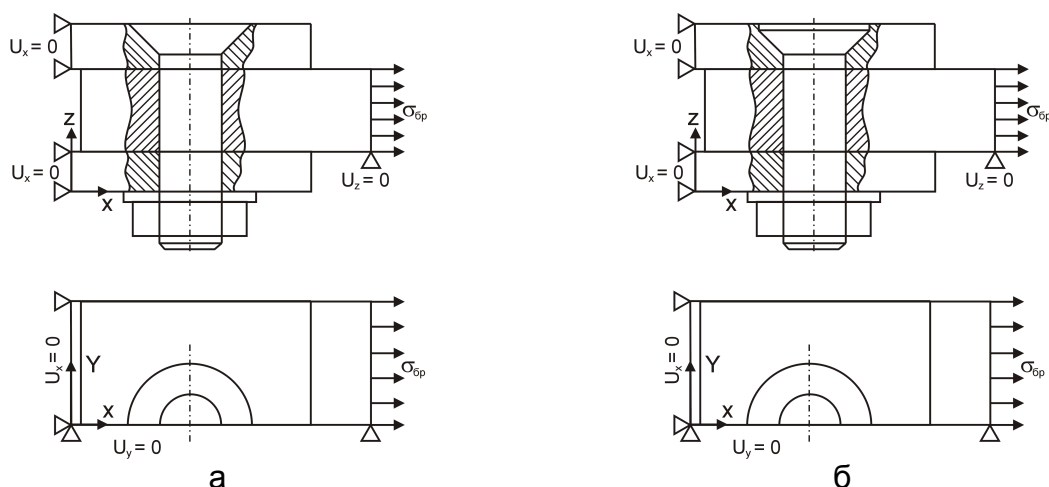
Расчетная схема двухсрезного одноболтового соединения
